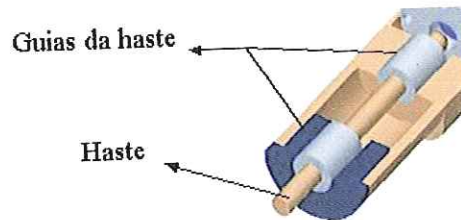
Detalhe interno da parte frontal do apalpador
